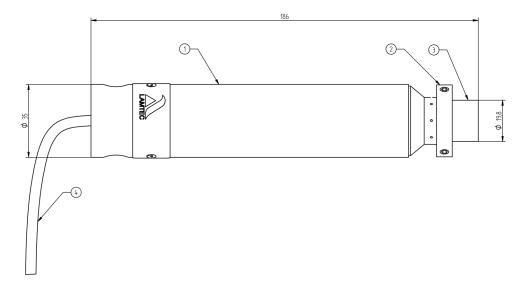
Sonde Combinée KS1D ECO (dimensions en mm)
